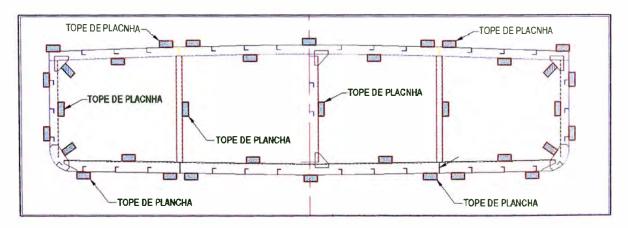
Galibo de Cuaderna Típica, mostrando la posición de los topes de planchas para su fabricación en serie.
